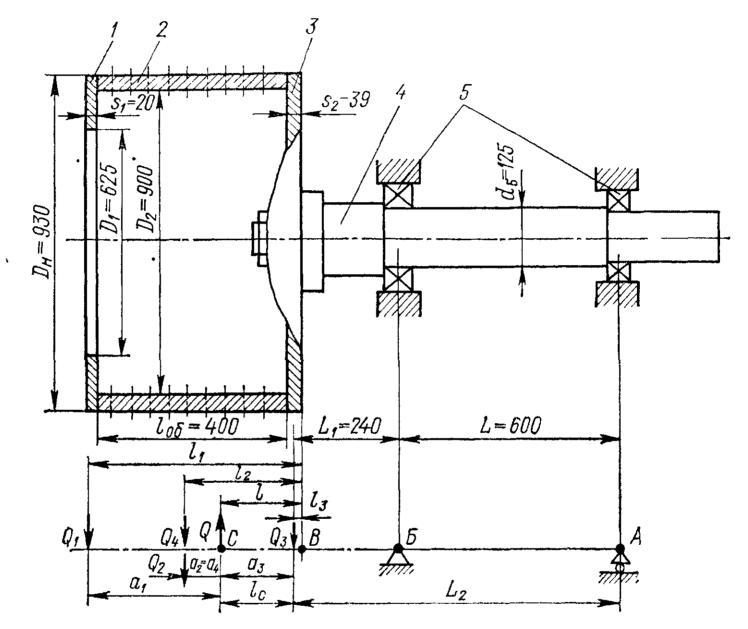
Ротор центрифуги и расчетная схема его консольного вала: 1 — плоский диск; 2 — обечайка; 3 — днище; 4 — вал; 5 — подшипник
